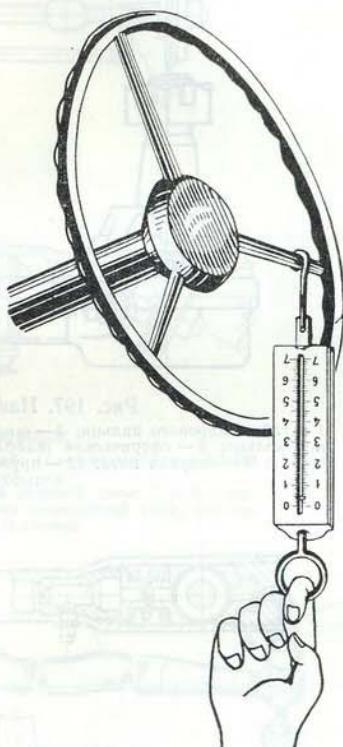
Проверка затяжки подшипников червяка при помощи динамометра
